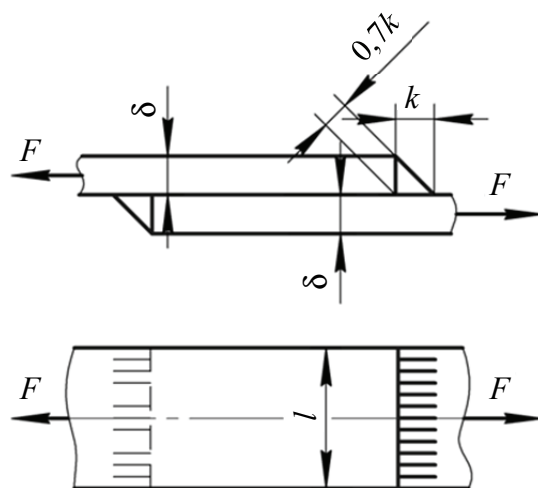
Сварное соединение угловым лобовым швом, нагруженное растягивающей силой
